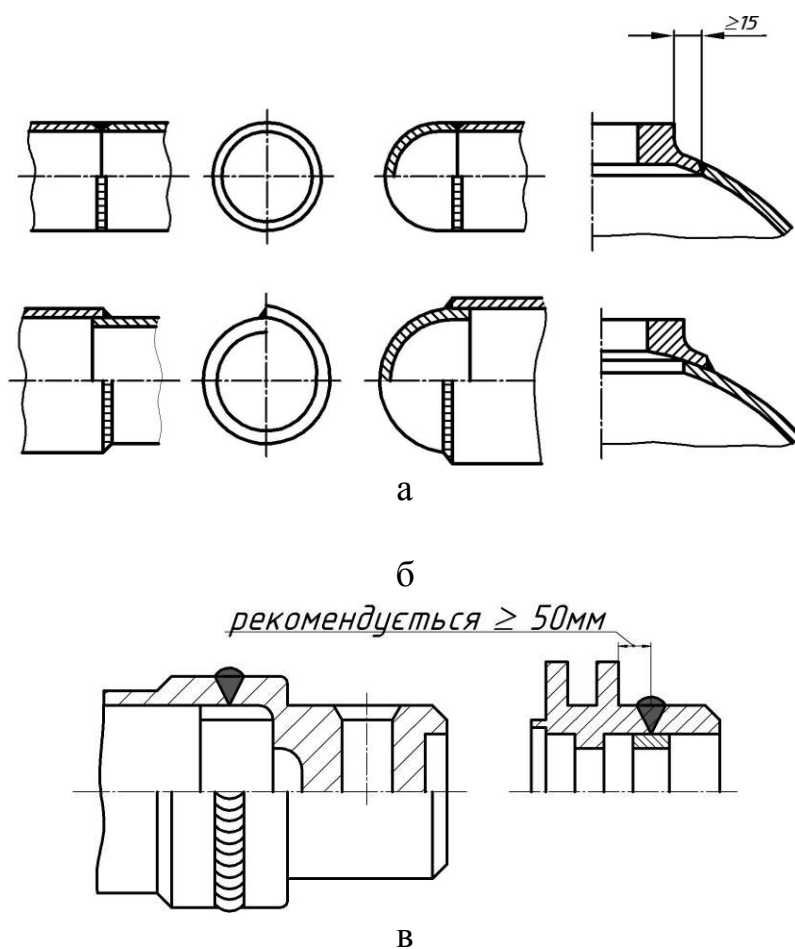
Типові конструкції, які одержують зварюванням плавленням
